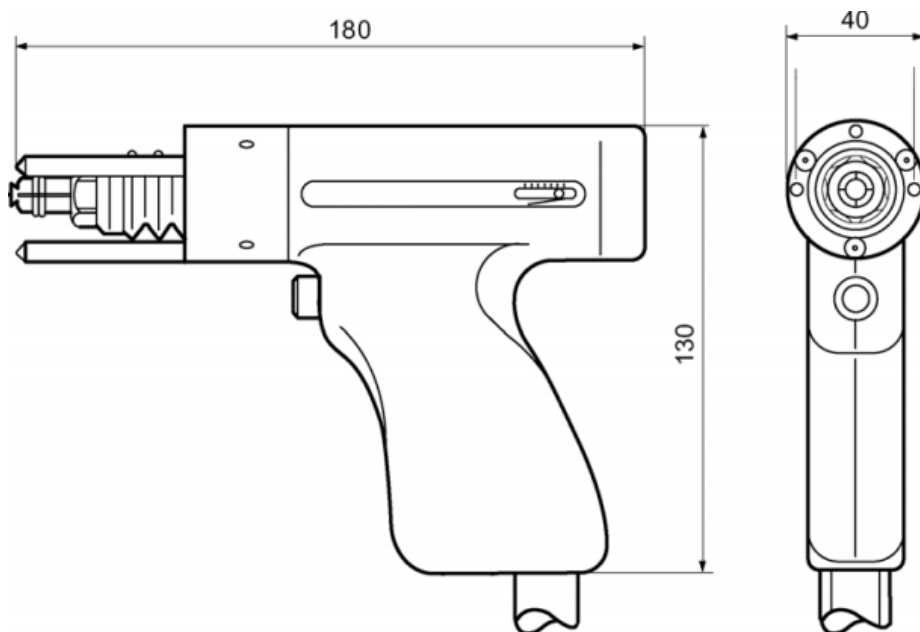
16 Размеры сварочного пистолета C0
